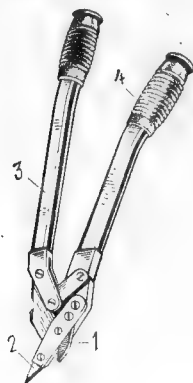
1 — режущая часть; 2 — носок; 3 — рычаг; 4 — ручка пластмассовая
